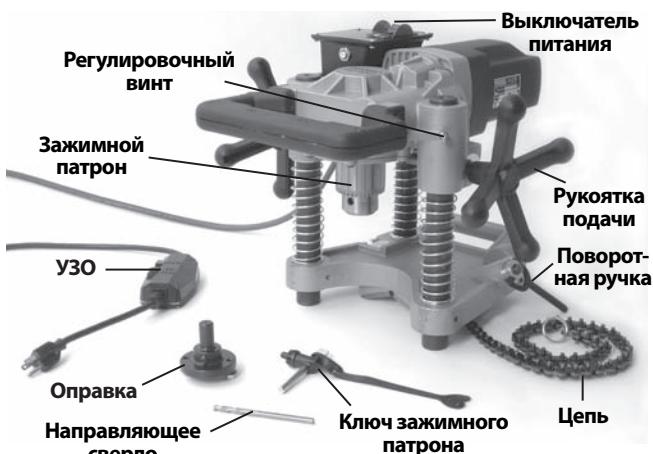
Модель HC-450 со стандартными принадлежностями
